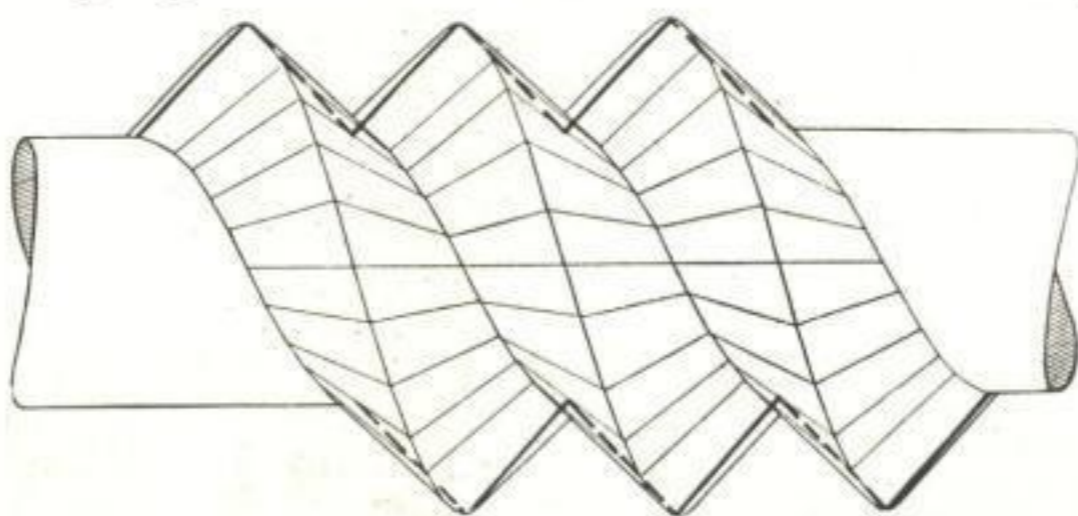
Draufsicht auf einen Gewindebolzen.
